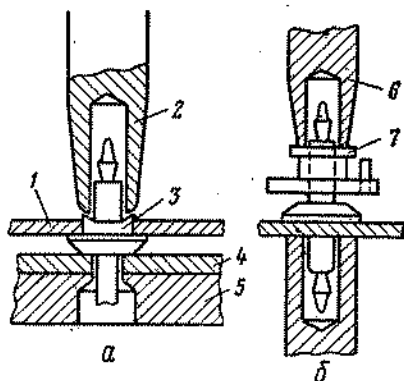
Способы запрессовки оси баланса и двойного ролика:
